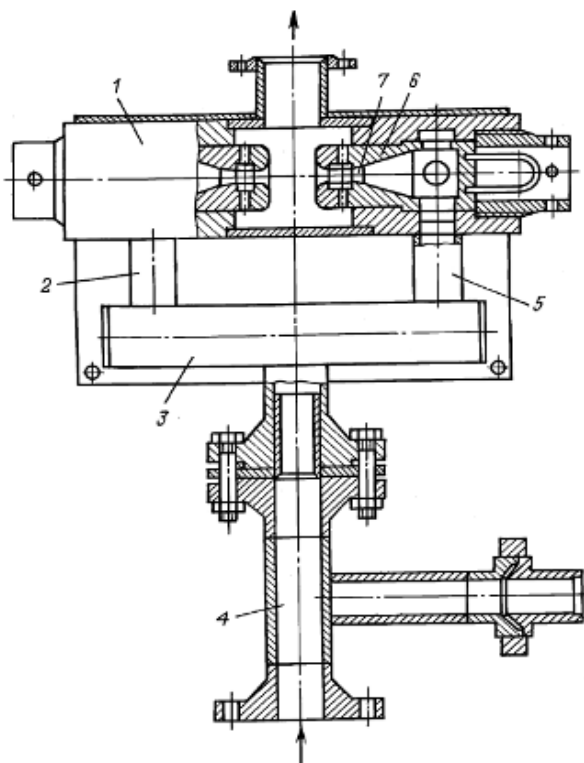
Диспергатор гидравлический ДГ-2 (1 — корпус диспергатора; 2, 5 — патрубки; 3 — коллектор; 4 — патрубок выходной; 6 — сопло; 7 — насадок)
